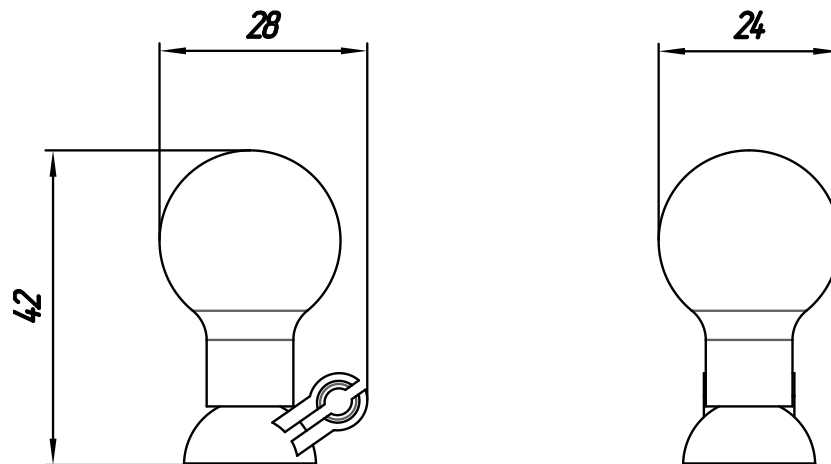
Габаритные размеры «Грудной детский ЭУП-06д (6 шт)»
